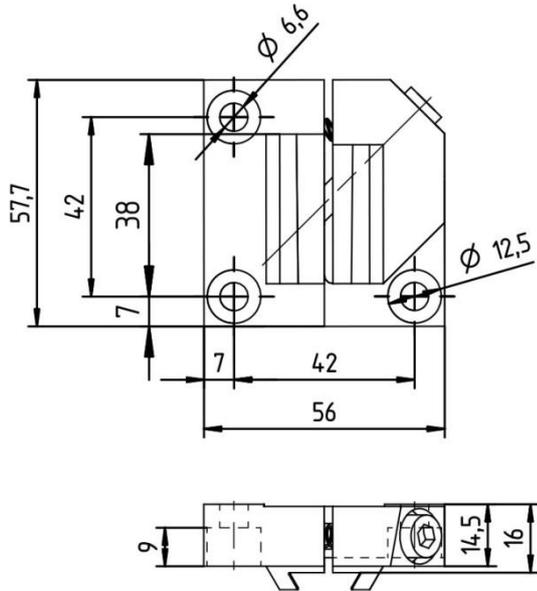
Maßzeichnung BE 901 FA-001 (alle Maße in mm)
